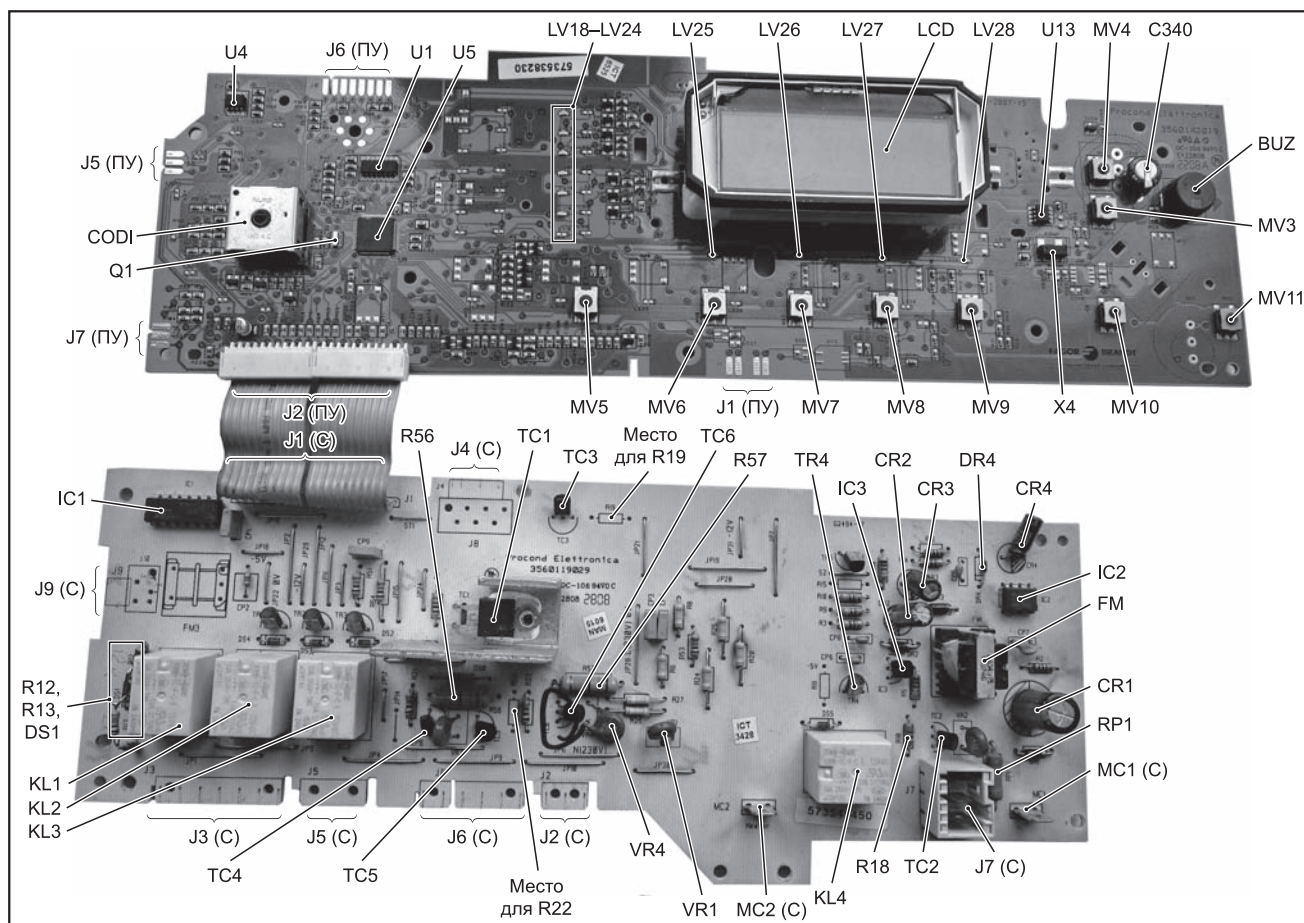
Внешний вид ЭМ СМ «BOSCH WOT245510E» и расположение на них основных элементов
